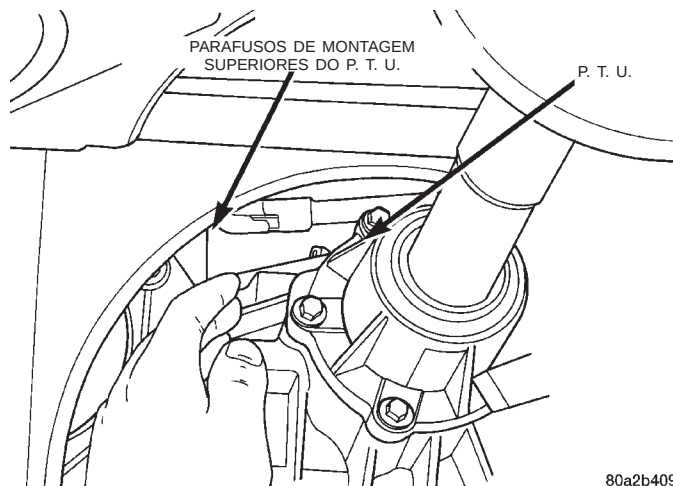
Parafusos de Montagem Superiores do P. T. U.
